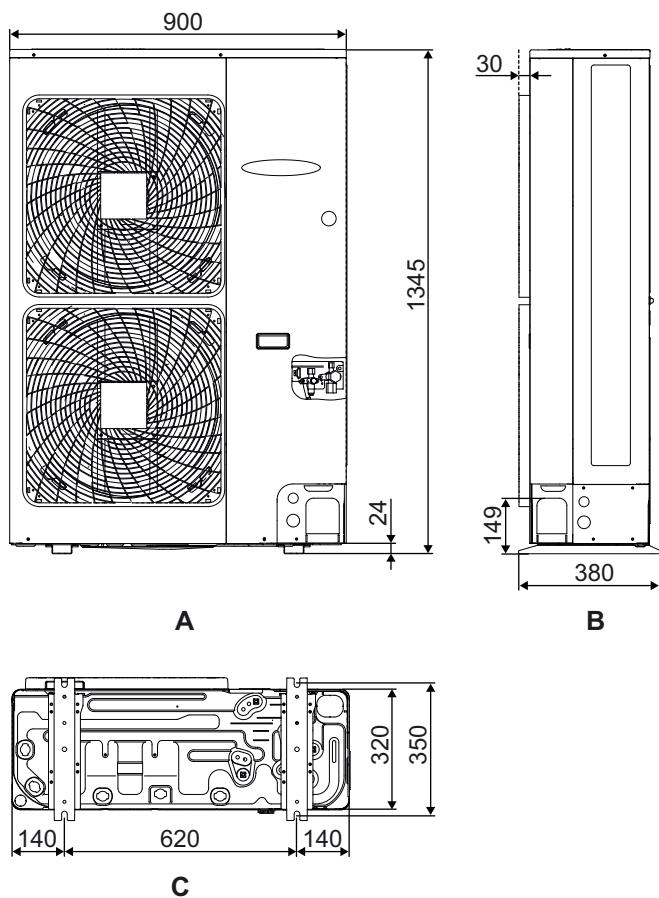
Draufsicht Außengerät RRLQ 4-8 kW
